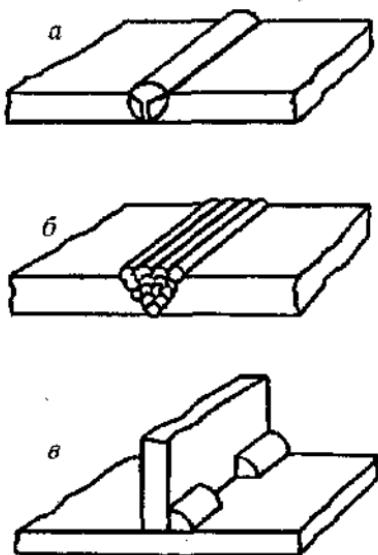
Некоторые типы сварных швов: а — стыковой непрерывный однопроходный, б — стыковой непрерывный многослойный; в — угловой прерывистый.
